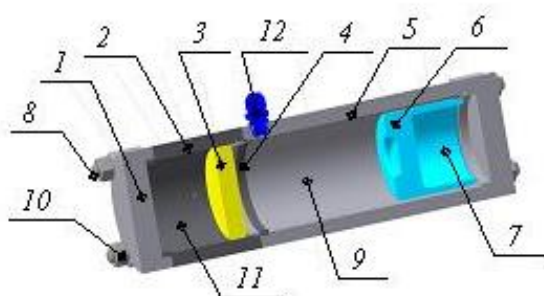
Ударный пневмоцилиндр: 1 – крышка; 2 – капсула для размещения крошки; 3 – передающая шайба; 4 – пояс; 5, 6 – поршень-ударник; 7 – взрывная камера; 8 – шпилька; 9 – пневматическая камера; 10 – гайка; 11 – ударная камера; 12 – штуцер для подвода сжатого воздуха
